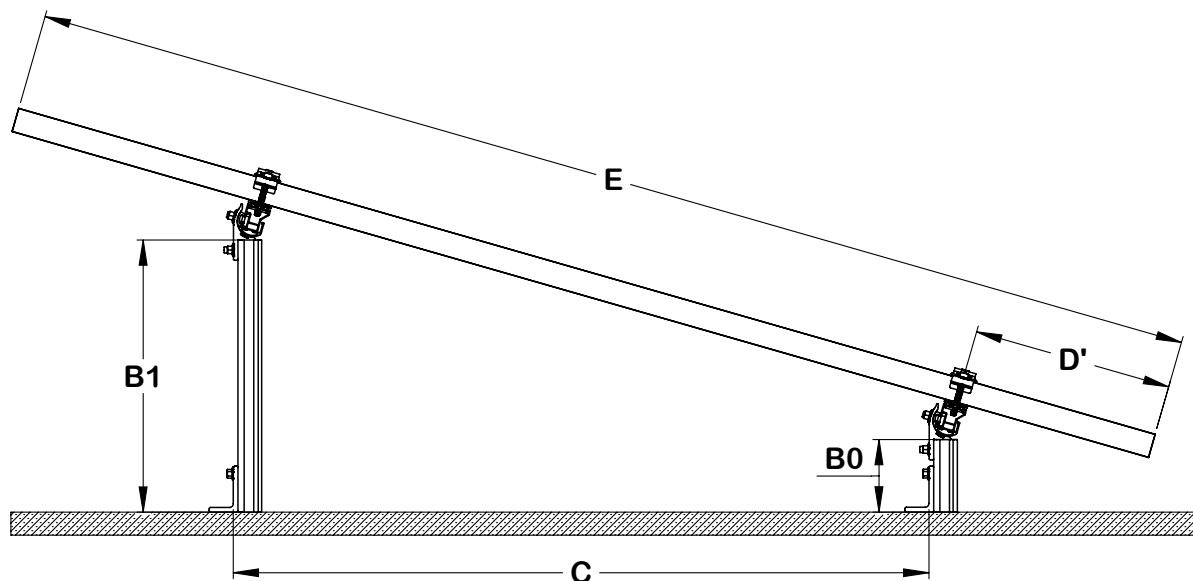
Dimensiones de ensamble para sistema Simple Tilt.
